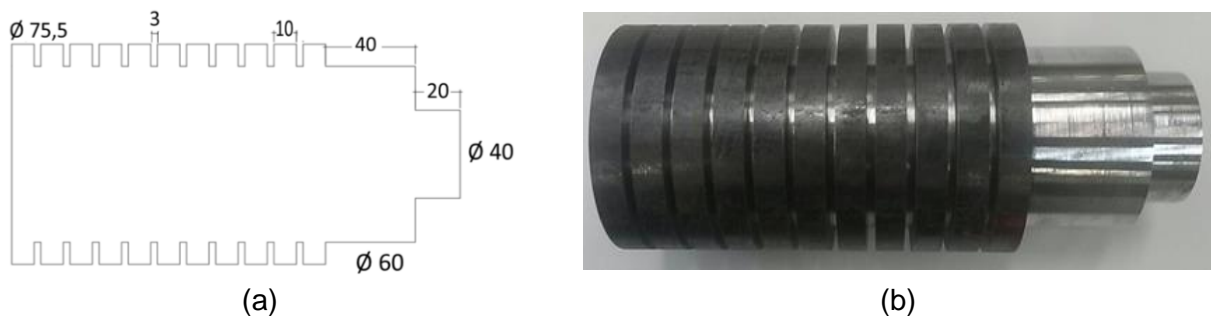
Características geométricas do corpo de prova preparado para os experimentos: (a) desenho contendo as dimensões [mm]; (b) imagem da peça antes de ser usinada.
